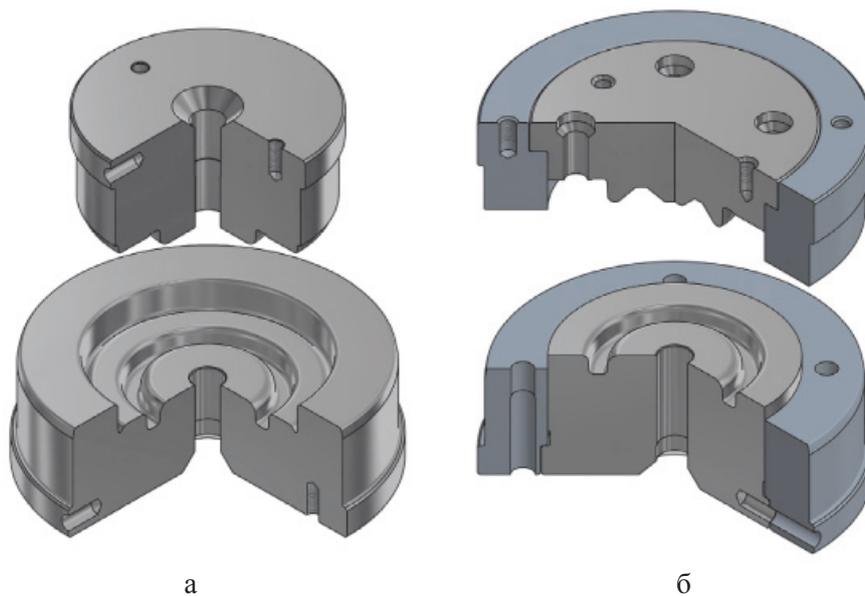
Конструкции деталей штампов предварительного (а) и окончательного (б) переходов, разработанные для штамповки поковки детали «Каретка синхронизатора» в соответствии с новой технологической схемой
